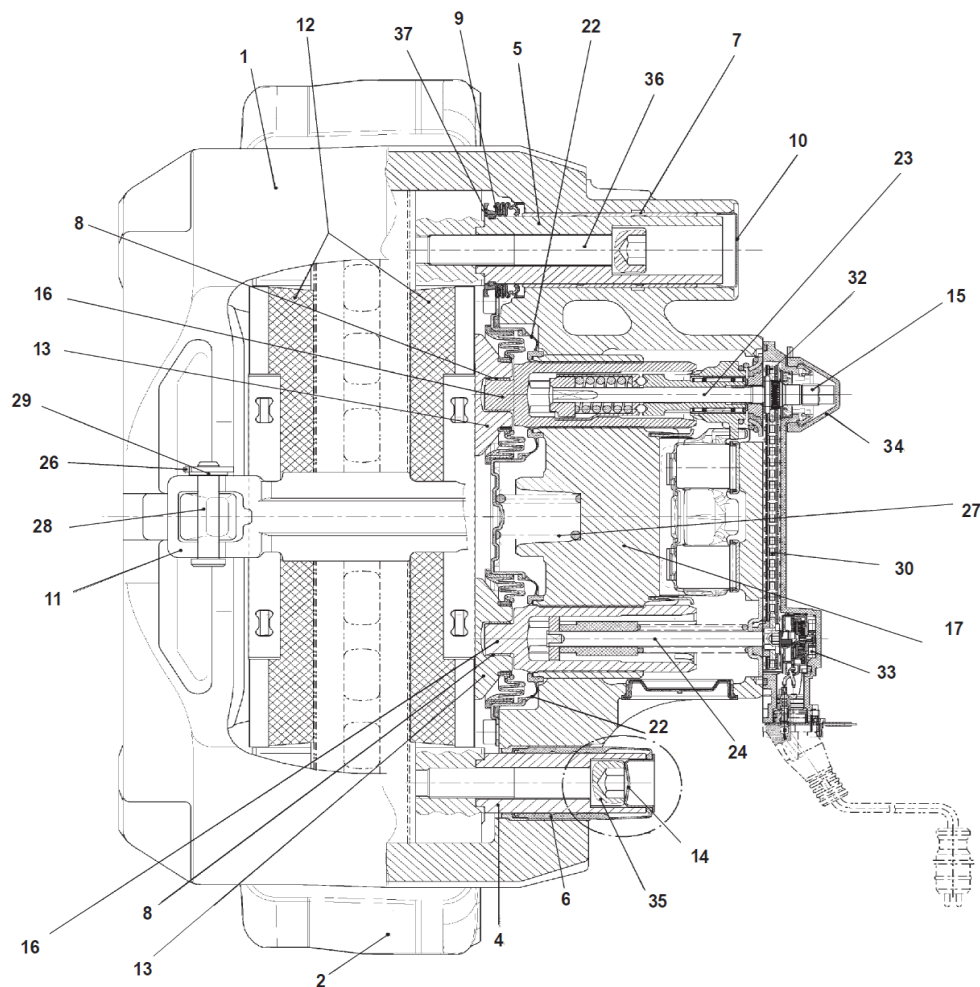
Общий вид тормозного механизма Knorr Bremse с пневмокамерой
